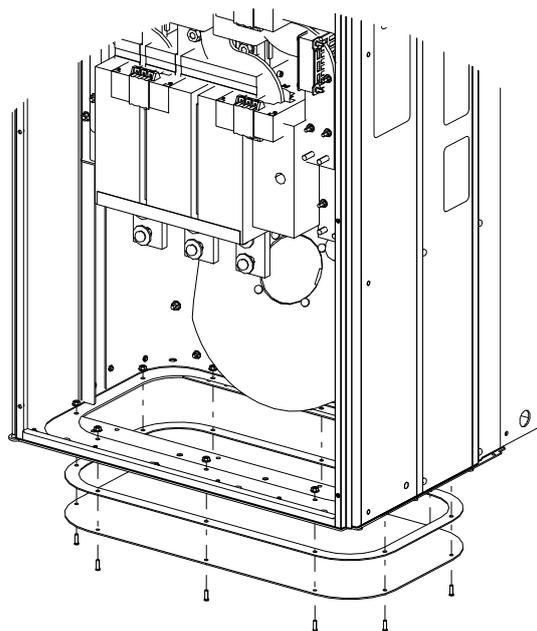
Gabinete metálico tamanho E1, vista inferior
